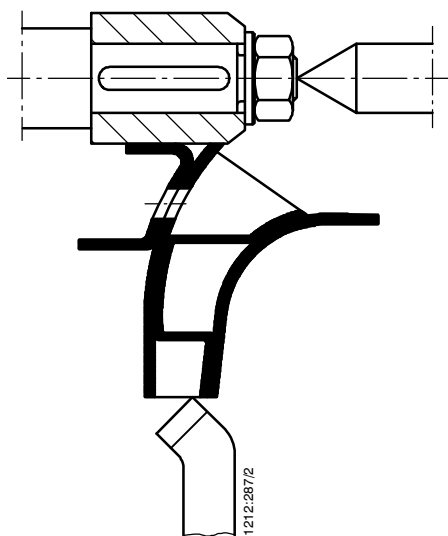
Обтачивание сварного колеса из хромникелевой стали
